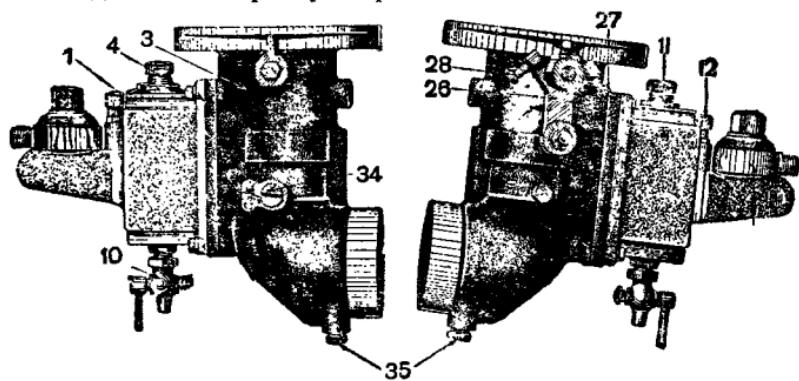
Общий вид карбюратора двигателя ЧТЗ.
